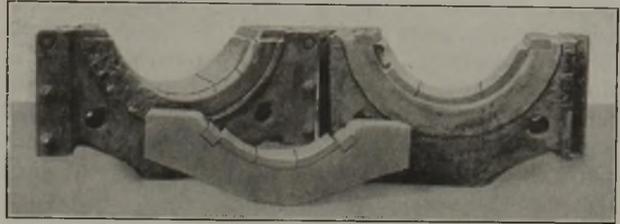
Einbaustücke einer Duo-Grobblechstraße, ausgefüttert mit mehrteiligen Kunstharz-Preßstoffabschnitten. Lagerkragen infolge eines Walzenzapfenbruchs beschädigt.
